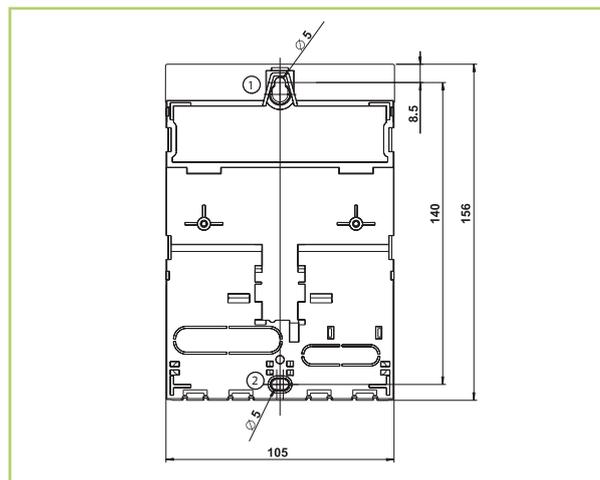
Rückseite des Reglers mit Montageöffnungen oben ① und unten ②
